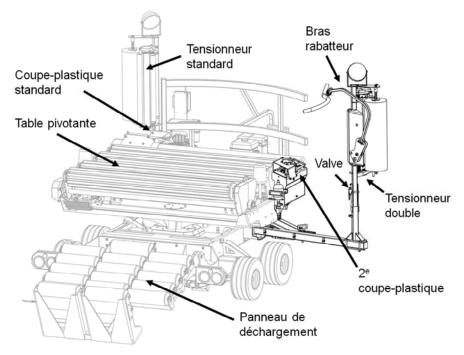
Tensionneur double installé sur une enrobeuse 780 SB
